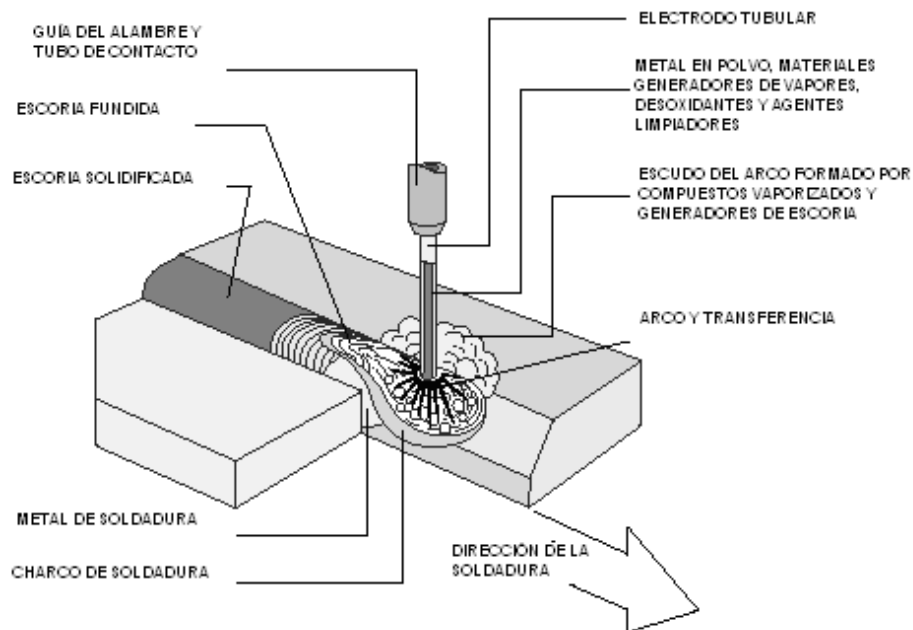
Soldadura por arco con núcleo de fundente y autoprotección
